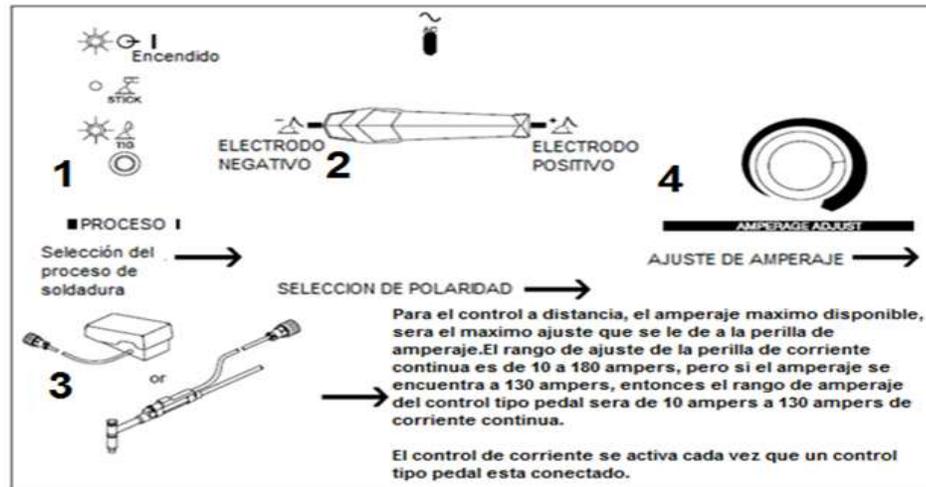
Pasos a realizar para un ajuste con soldadura TIG
